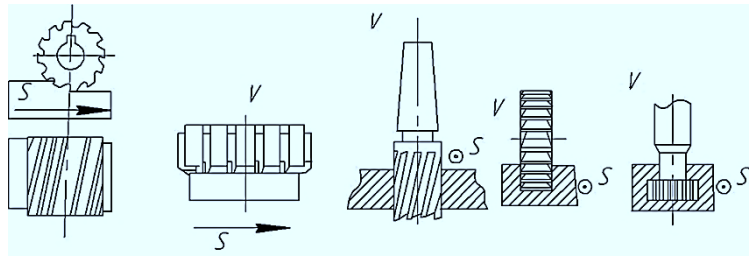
Фрези циліндричні (*a*), торцеві (*б*), кінцеві (*в*); тристоронні дискові (*г*), Т-твірні (*д*)
